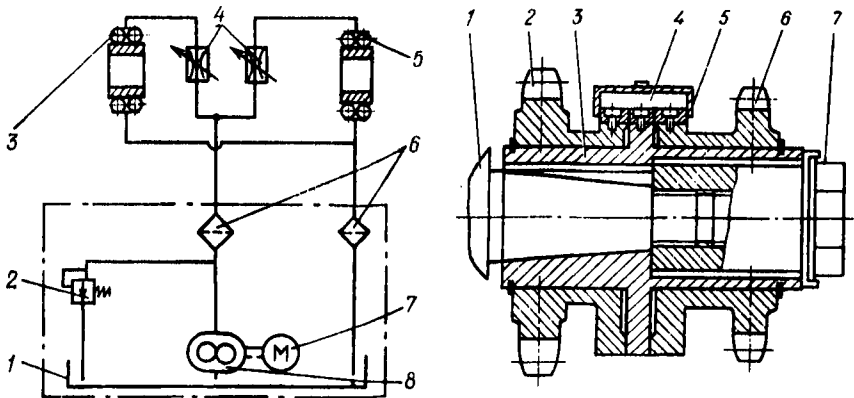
Конструкция муфты предельного момента привода механизма подачи: 1 — выходной вал редуктора; 2 — звездочка привода цепного контура механизма подачи; 3 — ведущий фланец муфты; 4 — предохранительная шпонка; 5 — крышка; 6 — звездочка привода цепного контура подающего конвейера; 7 — крепежный болт
